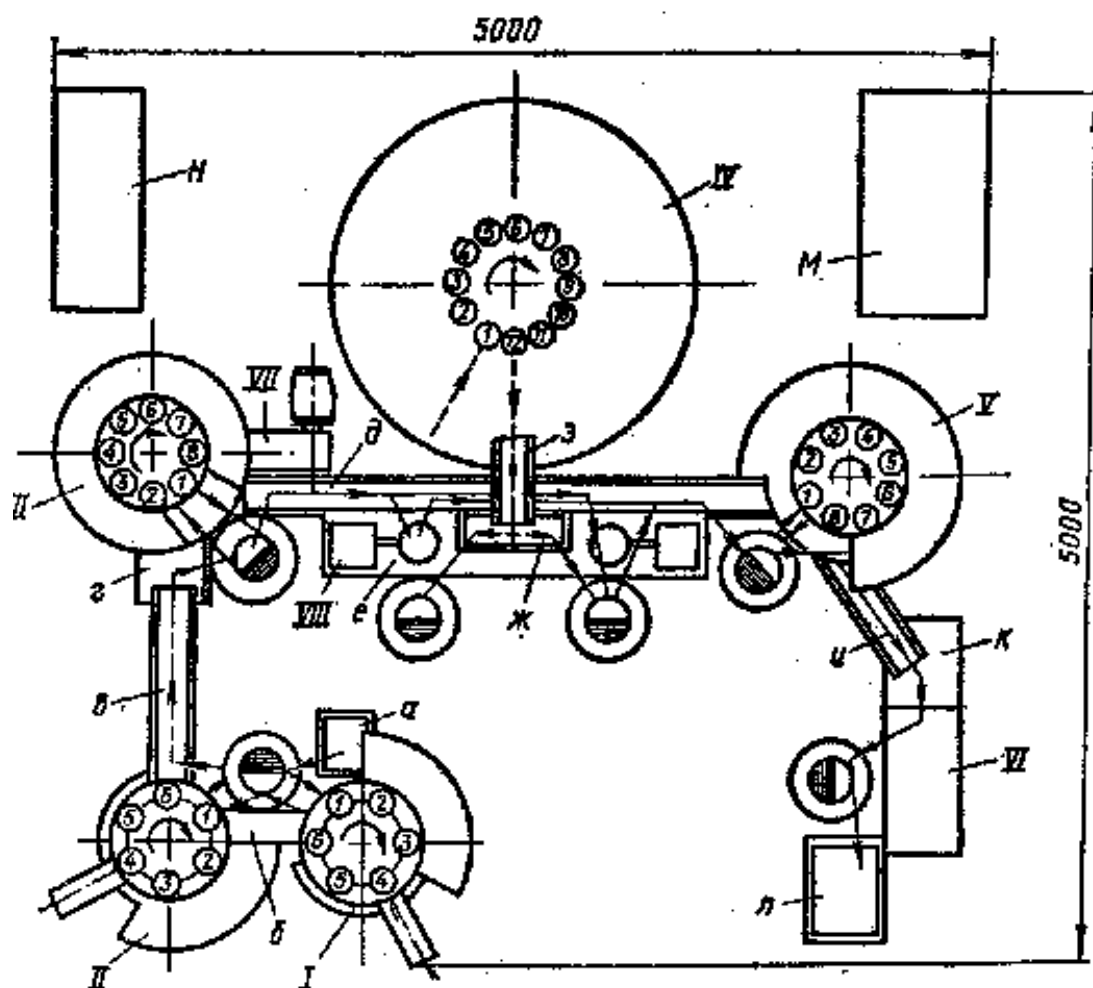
Схема автоматизированной линии сборки включателя стартера
